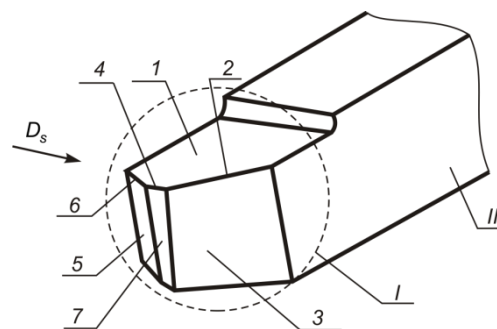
Элементы конструкции, поверхности и кромки на рабочей части лезвийных инструментов
